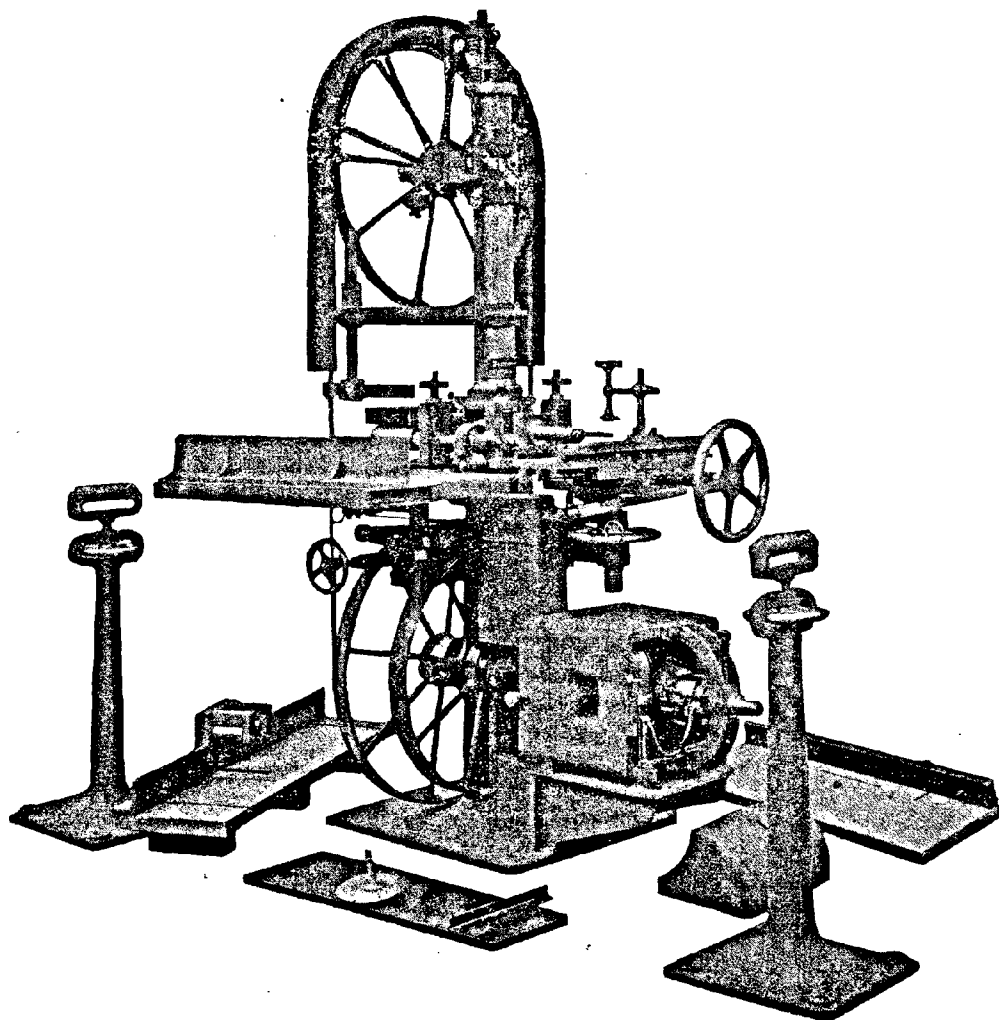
Machine universelle à travailler le bois des Ateliers d'Oerlikon.
